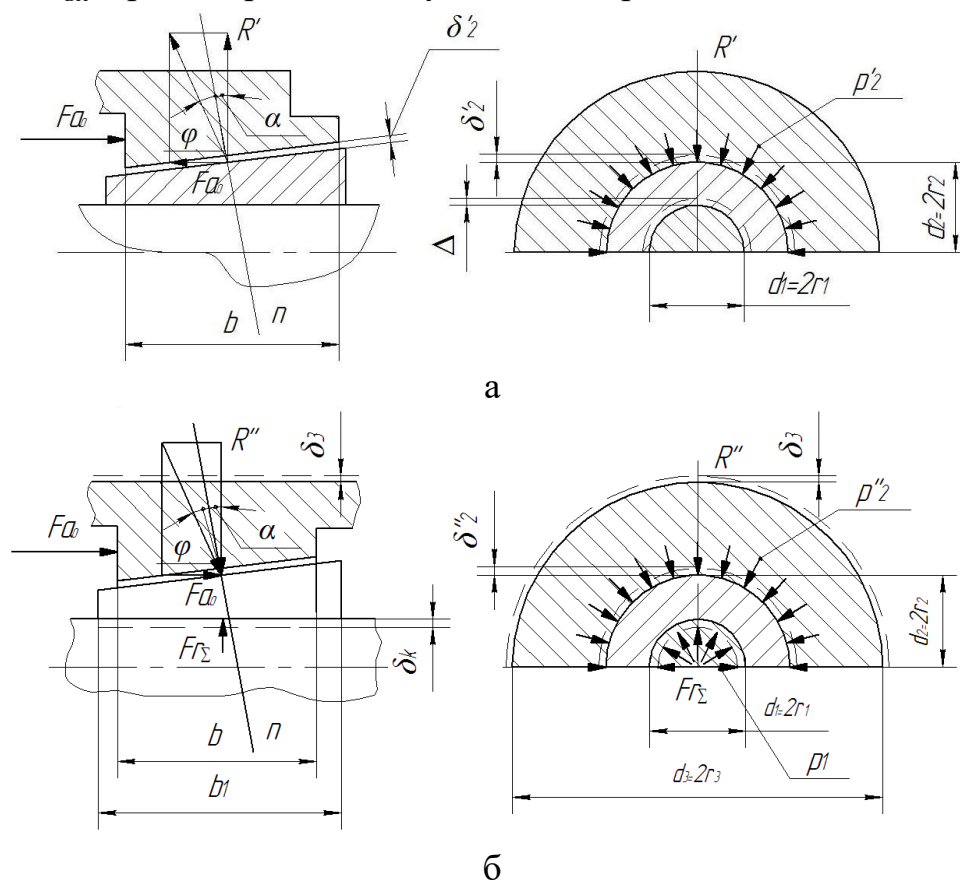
Розрахункові схеми для визначення пружних переміщень : а – вибірка зазору; б – натяг системи для отримання радіальної сили затиску інструмента
